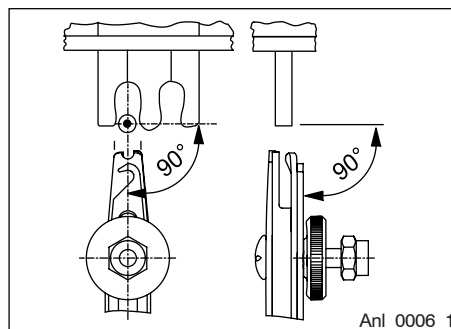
Anlegewerkzeug gerade anlegen / Fig. 4: Set termination tool straight
